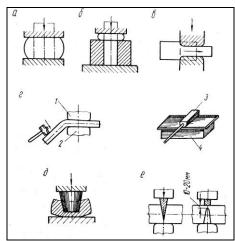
Операции ковки: а) осадка; б) высадка; г) протяжка; д) гибка; д) прошивка; е) рубка.
